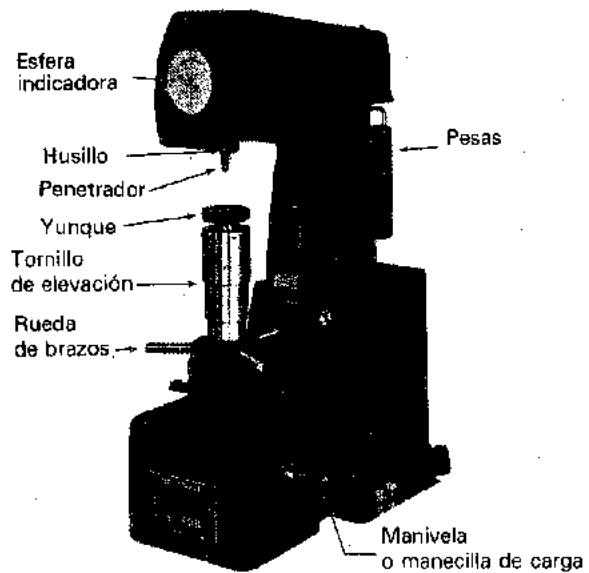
Máquina para ensayos de dureza Rockwell (Wilson Mechanical Instrument Division, American Chain and Cable Co., Inc.)
